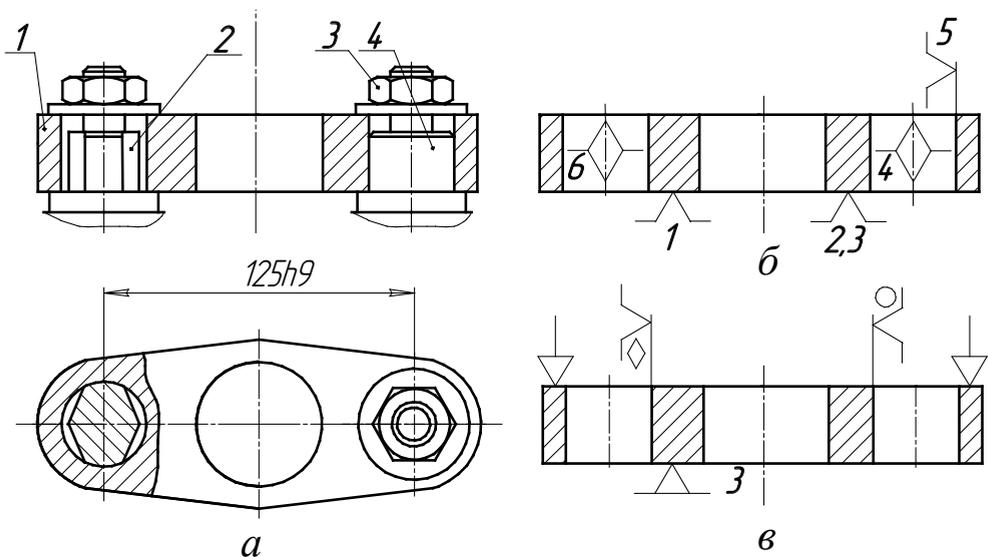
Установка заготовки на плоскость и два пальца:
